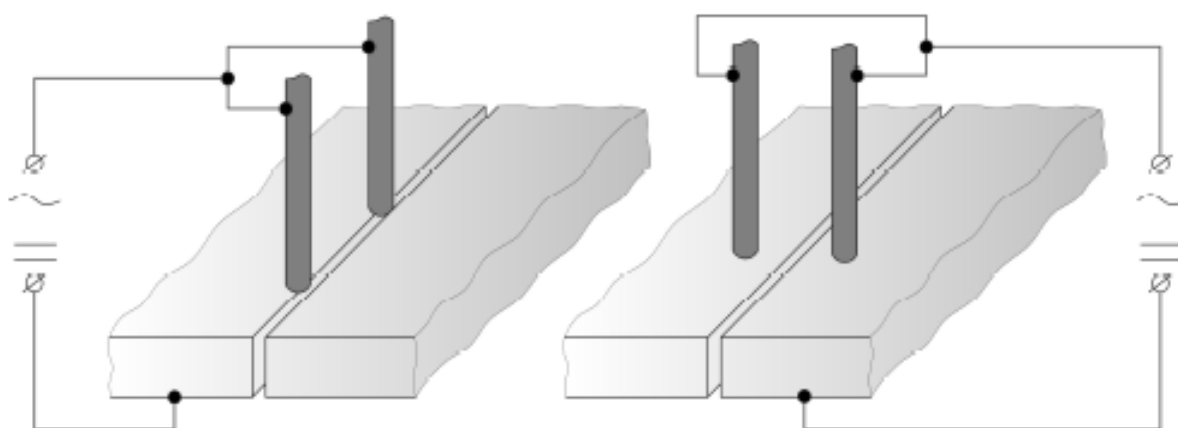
Расположение сварочных проволок при двухэлектродной сварке вдоль стыка (а) и поперёк стыка (б)
